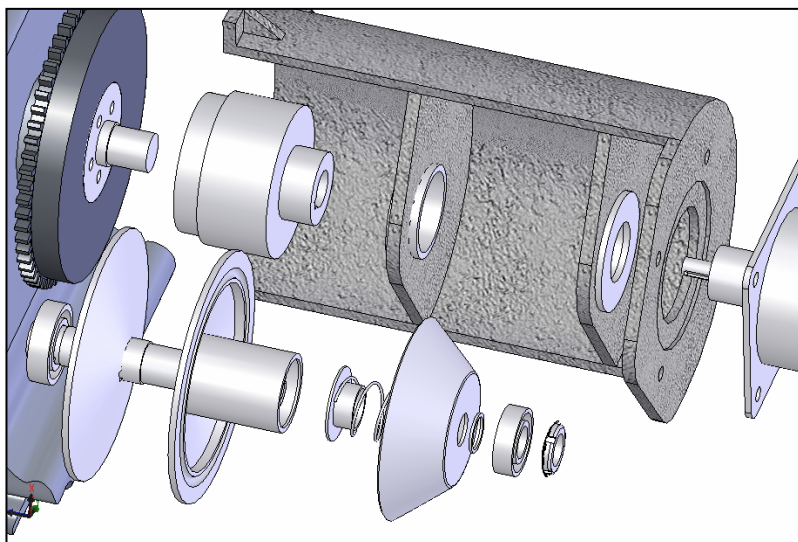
Vista explosionada del acoplamiento del motor eléctrico
